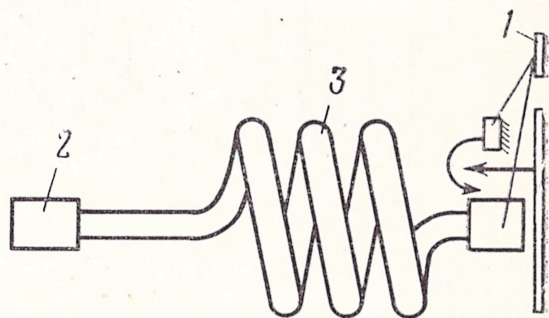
Схема укладки кабельного ствола в бухту (начало укладки у неподвижного разъема).
